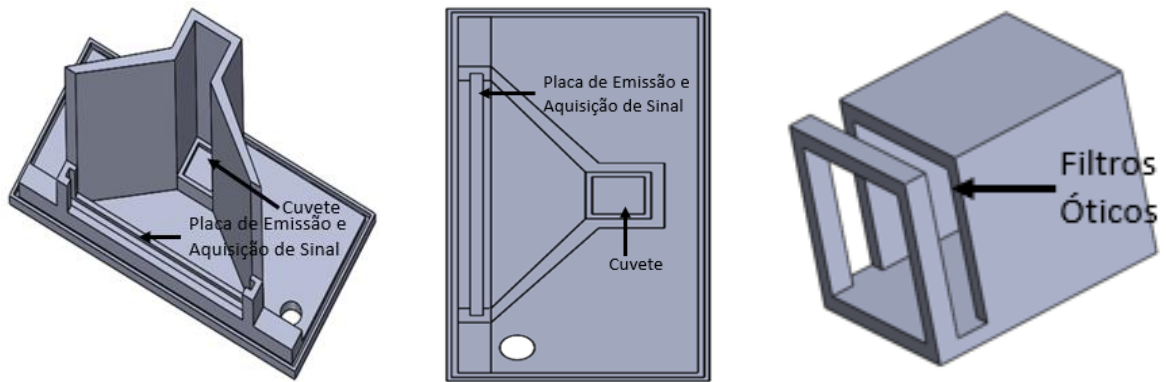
Proposta de encapsulamento desenhada em CAD para a PCB que contém o sistema de iluminação e o sistema de aquisição e tratamento de sinal integrados.
